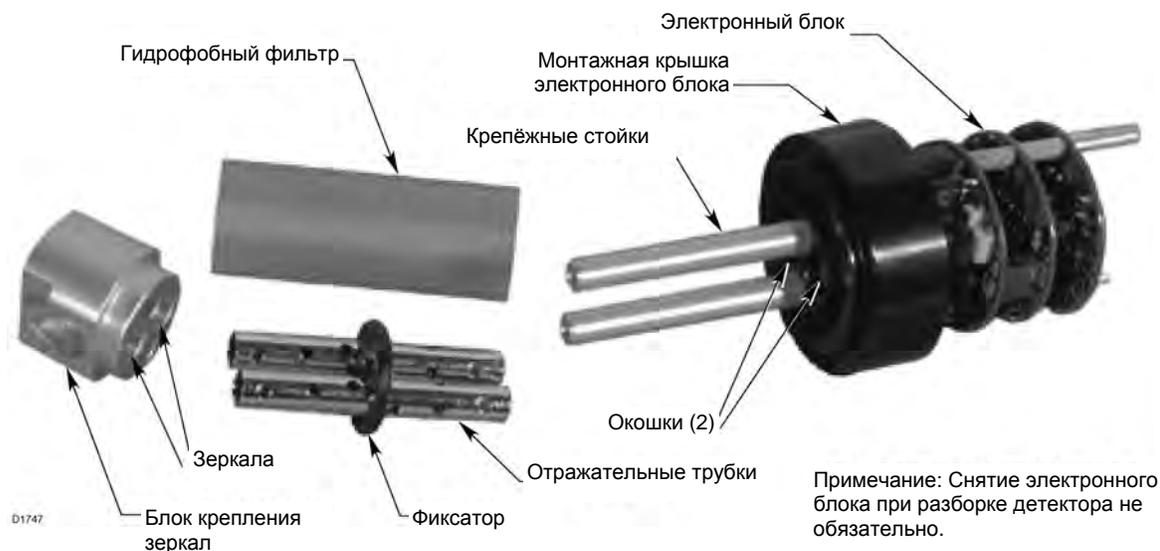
Разборка детектора PIR9400 в алюминиевом корпусе для проведения чистки.
